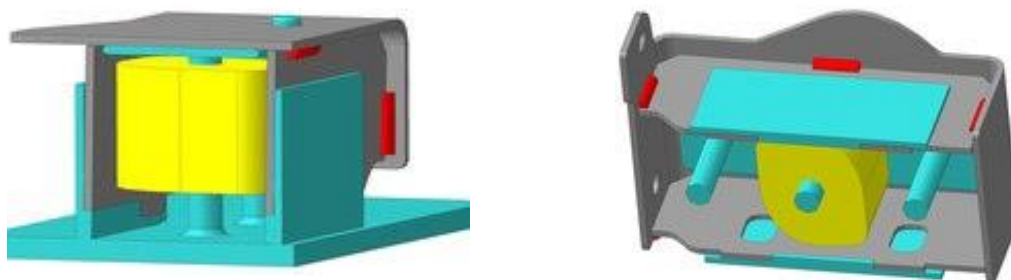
Схема сборки-сварки с механизированным эксцентриковым прижимом
